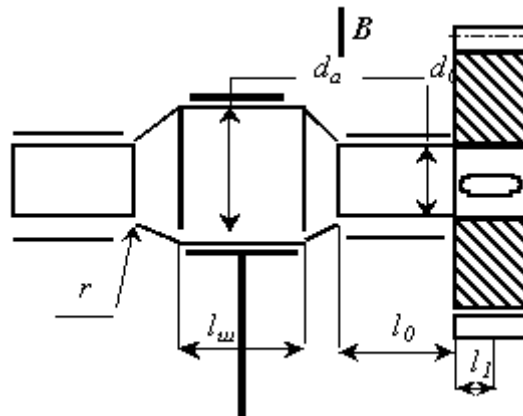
Розрахункова схема для визначення зусилля на повзуні, що допускається міцністю вала.
